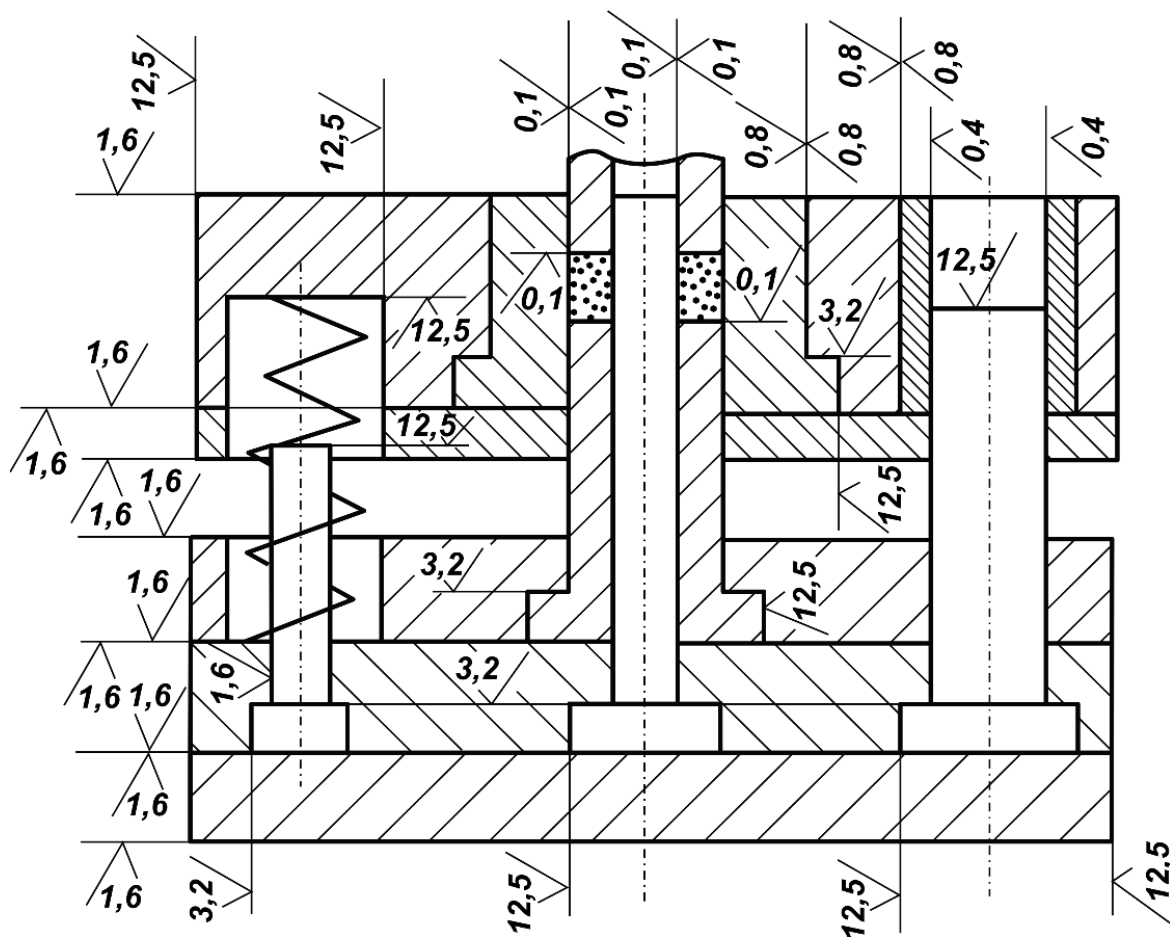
Шероховатость поверхностей деталей пресс-форм
